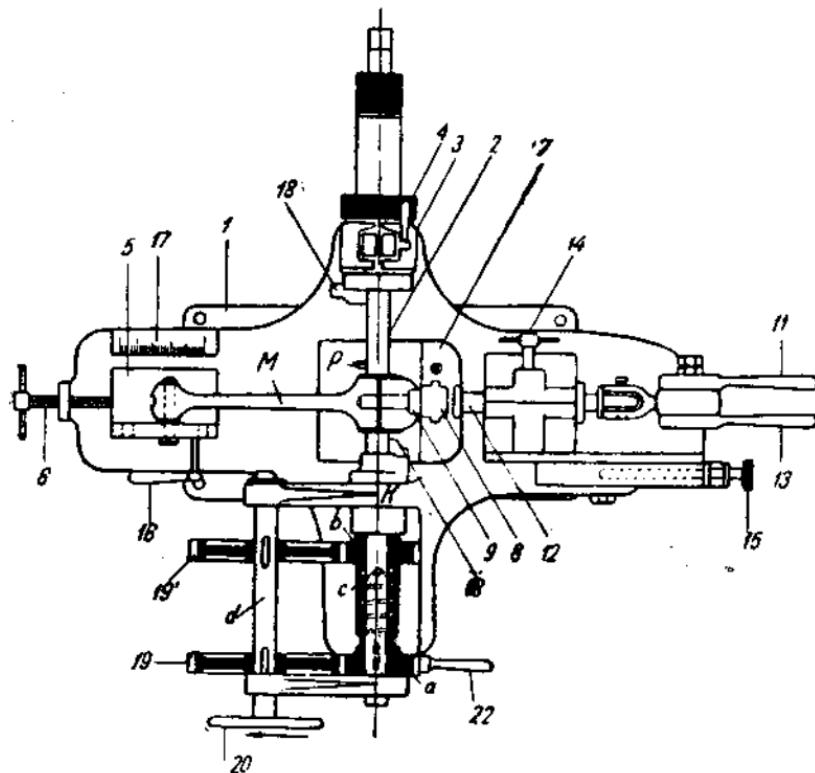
Прибор «Хемпи-Купер С-70» для расточки шатунных подшипников.
